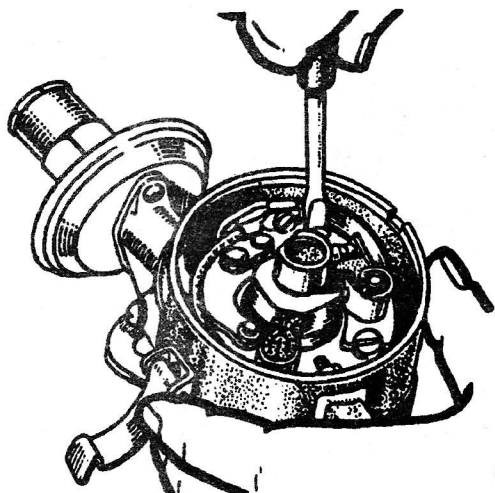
Отвертывание стопорного винта для регулировки зазора между контактами
